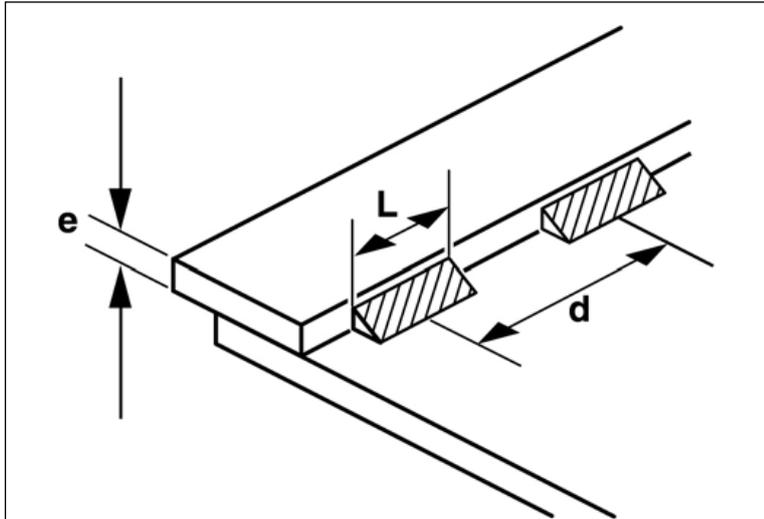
Cotes pour le soudage d'agrafage
